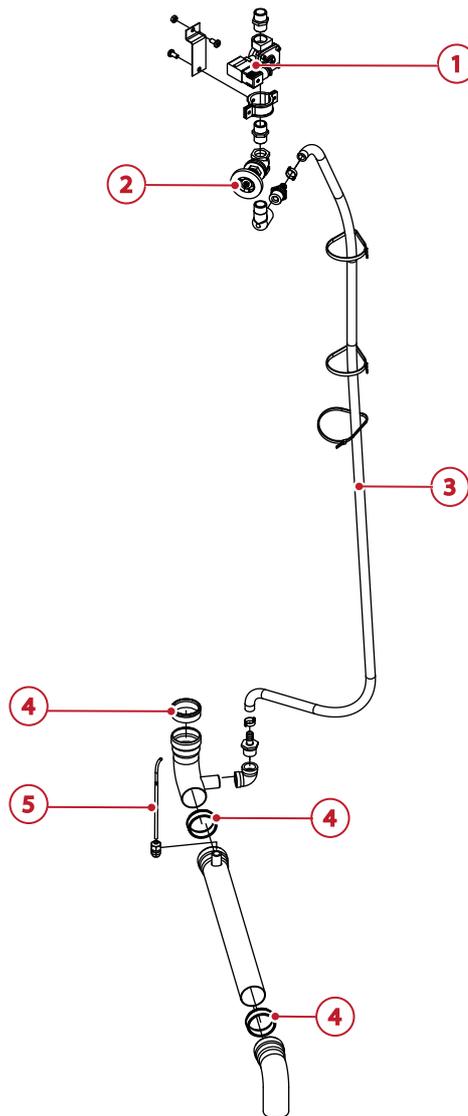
Übersicht Maschinenablauf mit Abwasserkühlung
